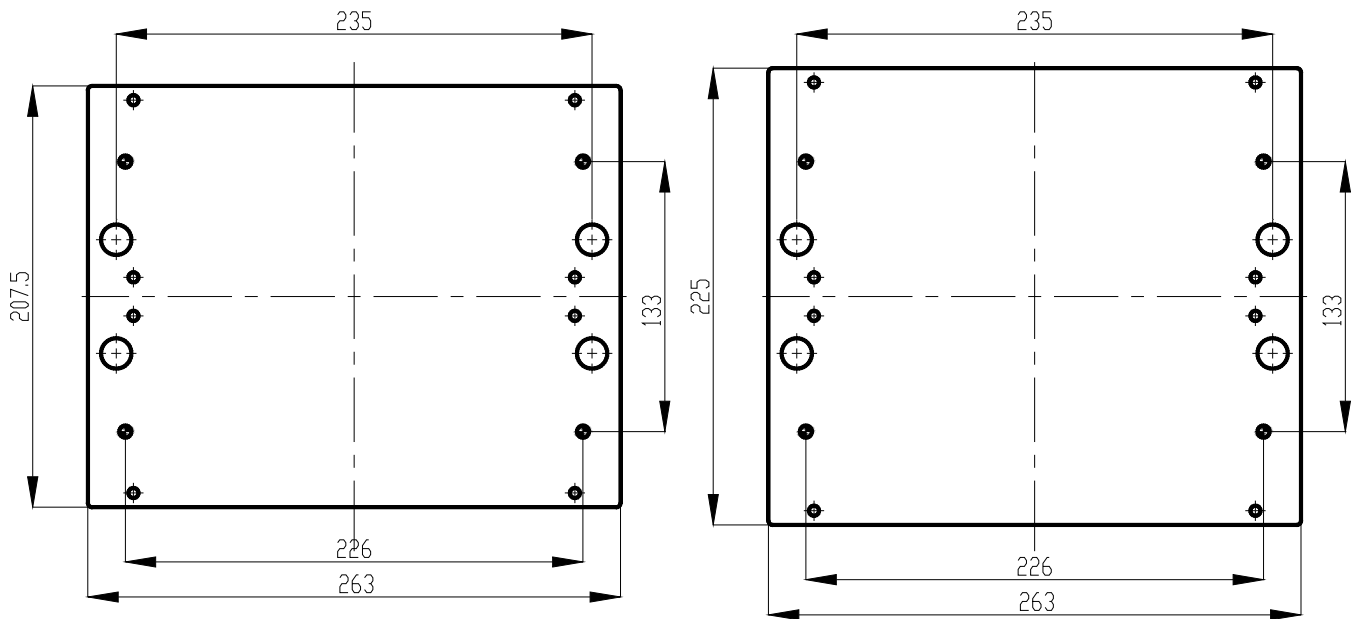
Габаритные и установочные размеры панели реакторов ЕИУС.468266.003.027
